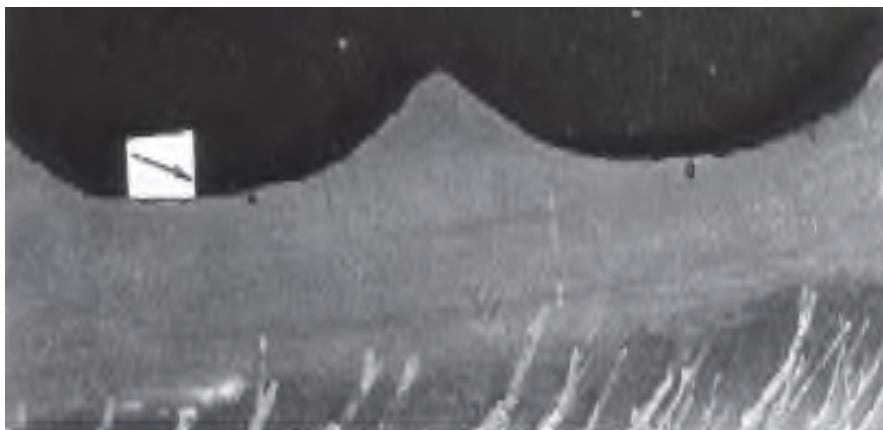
Підкіркові бульбашки біля поверхні листового зливка масою 27 т (поперечний розріз зливка) [24]
